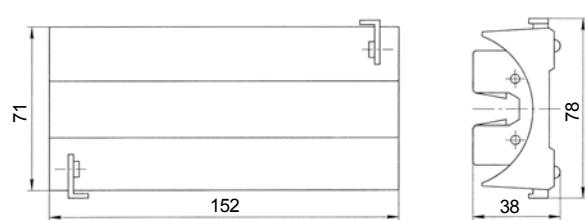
Габаритные размеры крышки холостой типа КХ 6.
